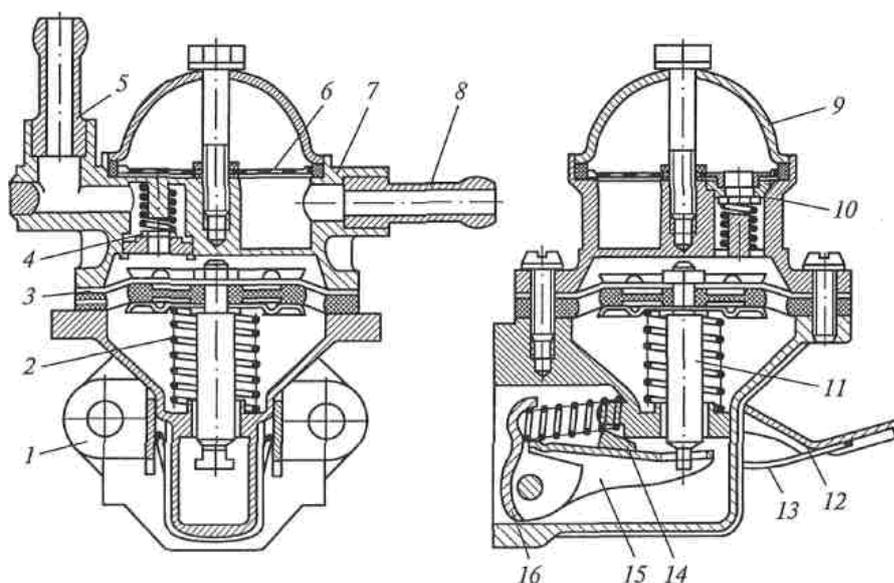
Топливный насос: 1,7 - части корпуса; 2, 13 - пружины; 3 - блок диафрагм; 4, 10 - клапаны; 5,8 - патрубки; 6 - фильтр; 9 - крышка; 11 - шток; 12, 16 - рычаги; 14 - эксцентрик; 15 – балансир
